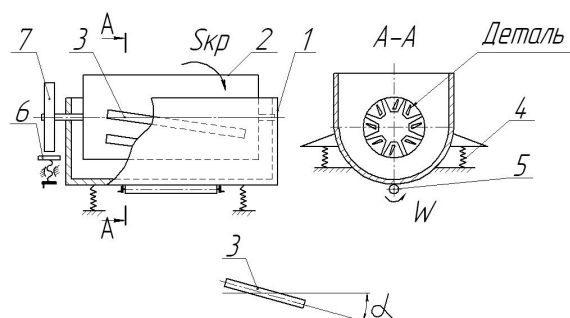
Технологическая схема виброударной упрочняющей обработки длинномерных деталей: 1 – рабочая камера; 2 – приспособление; 3 – обрабатываемая деталь; 4 – пружина спиральная; 5 – вибратор; 6 – тормозной башмак; 7 – барабан приводной
